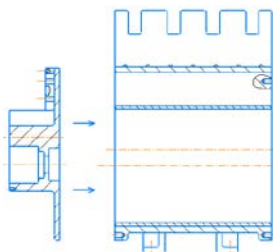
Схема присоединения крышки под ведомые валы к корпусу комбинированного насоса
